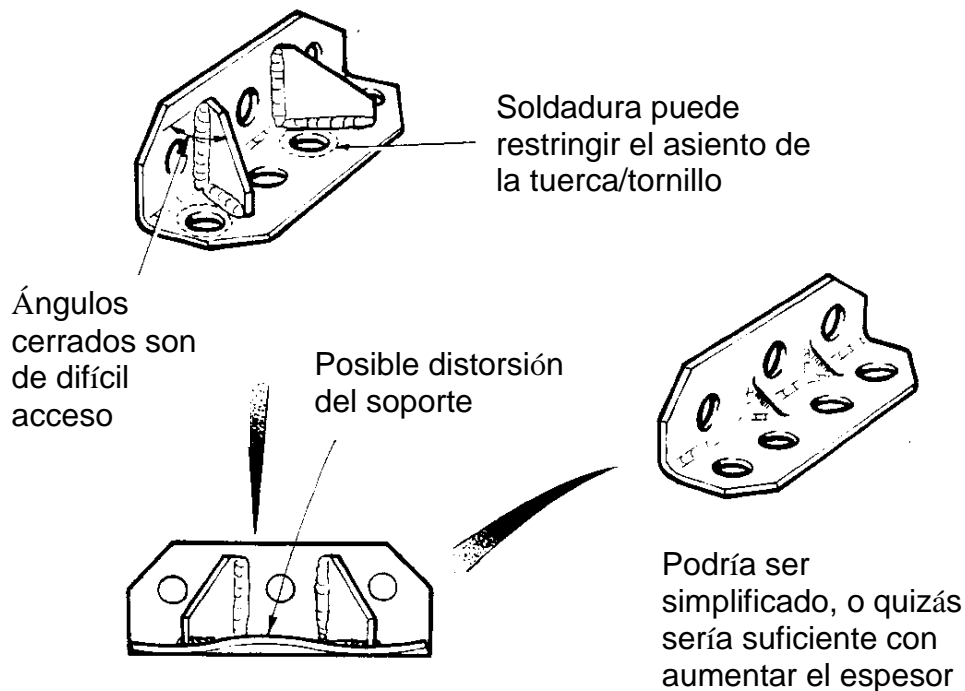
Desventajas de un soporte con soldaduras
